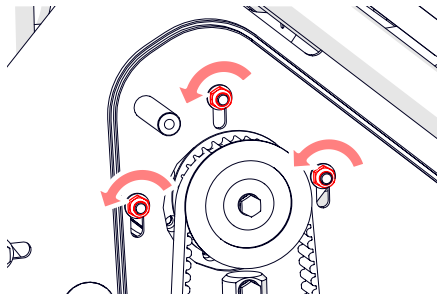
B - 3 obere Muttern des Motors leicht lösen.
